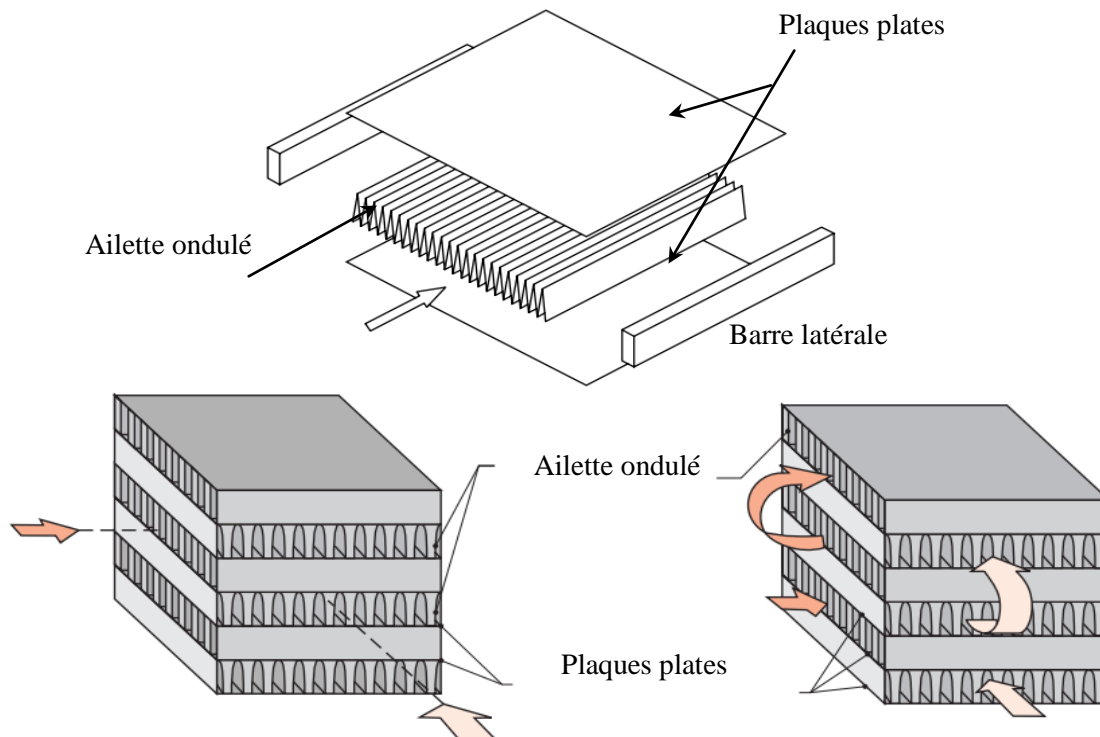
Echangeur thermique à plaques et ailettes (a) vue éclatée et (b) l'arrangement d'écoulement à courant croisé Çengel [9].
